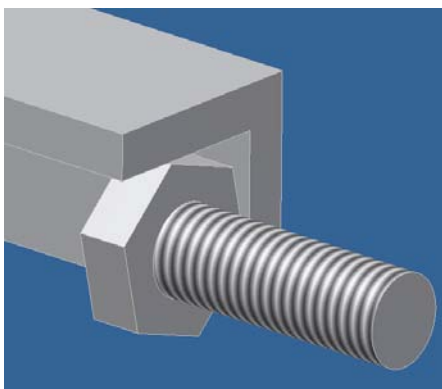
4. 5. 2. Perno soldado al extremo
